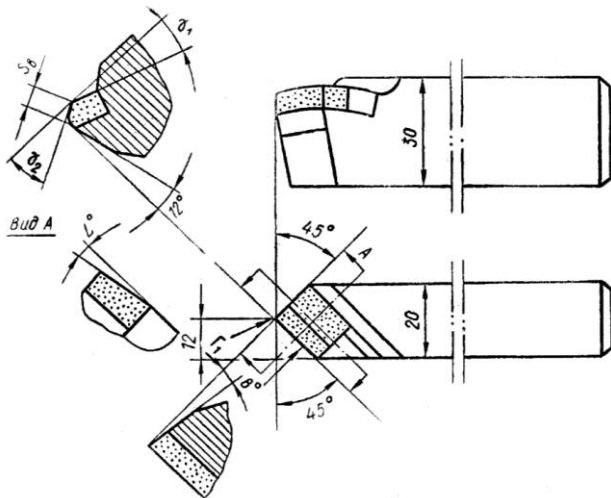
Геометрія різальної частини різця для точіння наплавленого металу
